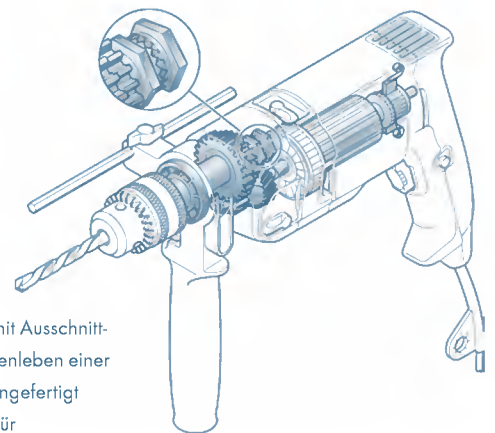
Detailansicht mit Ausschnittvergrößerung
